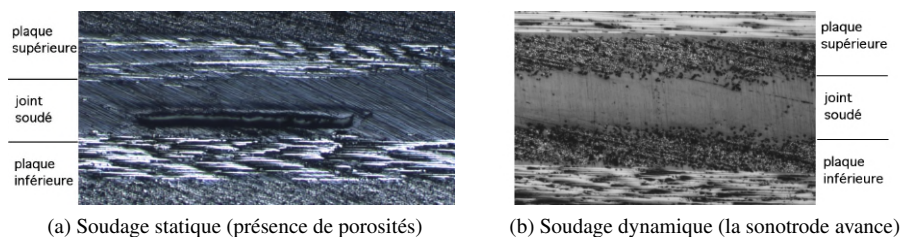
Coupe microscopique d'un joint soudé.
